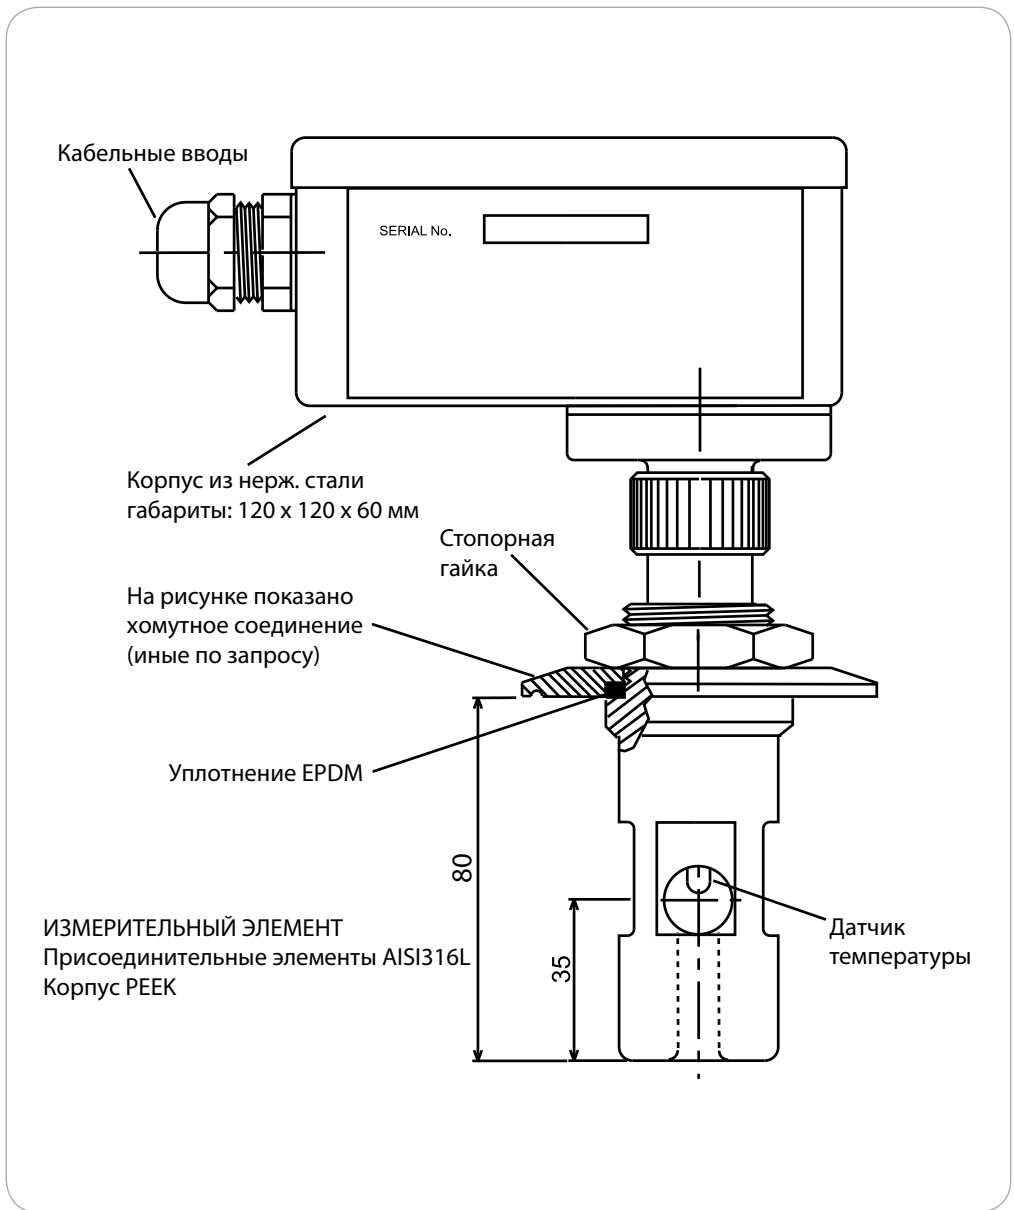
Габаритные размеры датчика IET40L с хомутным присоединением (вид сбоку)
